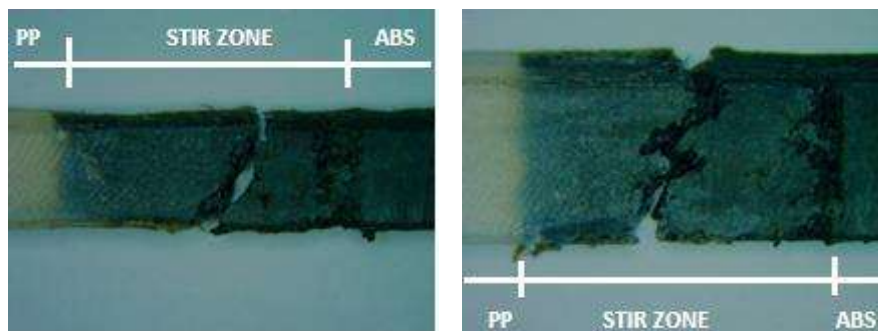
Probetas fracturadas mediante ensayo de tensión.
